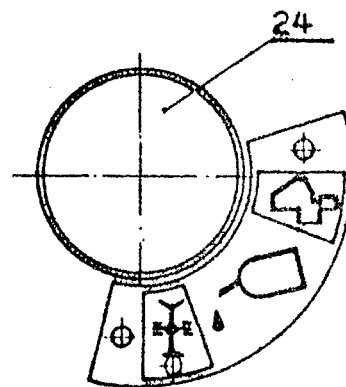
Distributeur de graissage /glissière - engrenages/
